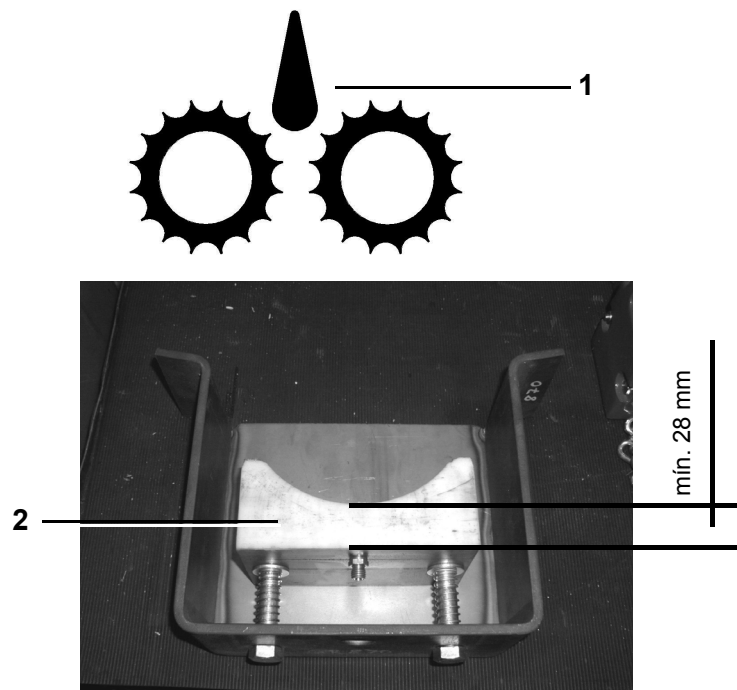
Lubrificação da lâmina de desgaste deslizante de plástico do anel de giro
